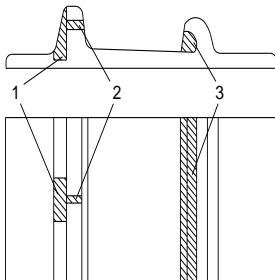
Заготовка подкладки для крепления типа «Метро»: (штриховкой показаны места выфрезеровки в условиях строительных организаций):
